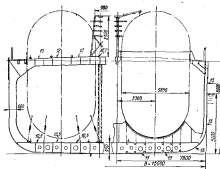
Поперечный разрез корпуса цистерны «Petrolcar» Orefes.
